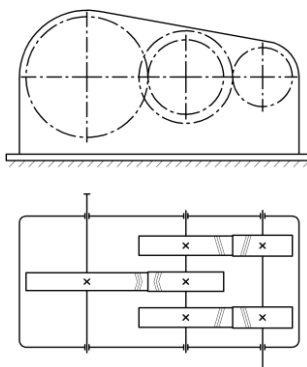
Двухступенчатый горизонтальный редуктор с раздвоенной быстроходной ступенью
